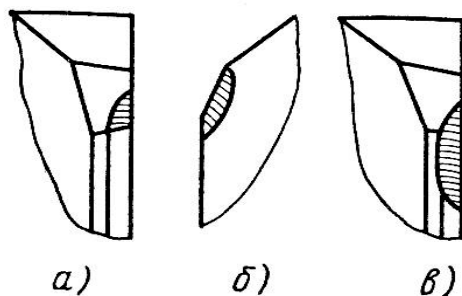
Схема износа развёртки из быстрорежущей стали:
